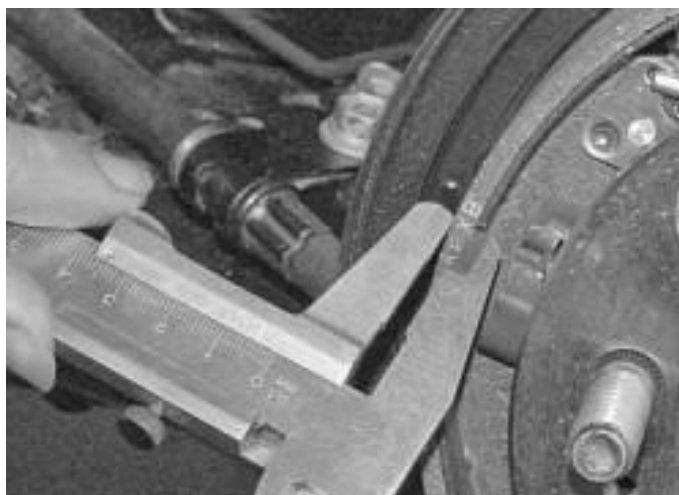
Вимірювання товщини фрикційних накладок штангенциркулем
